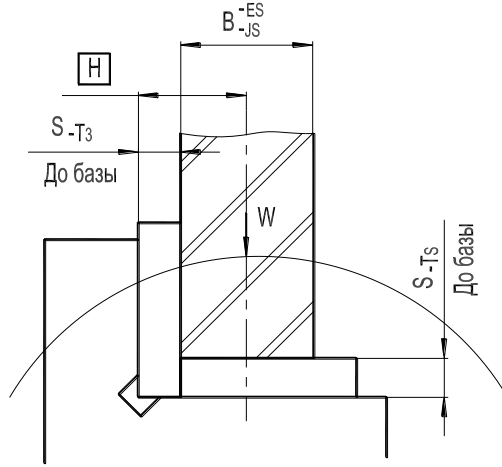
Схема настройки інструменту при фрезеруванні шпонкового паза.
